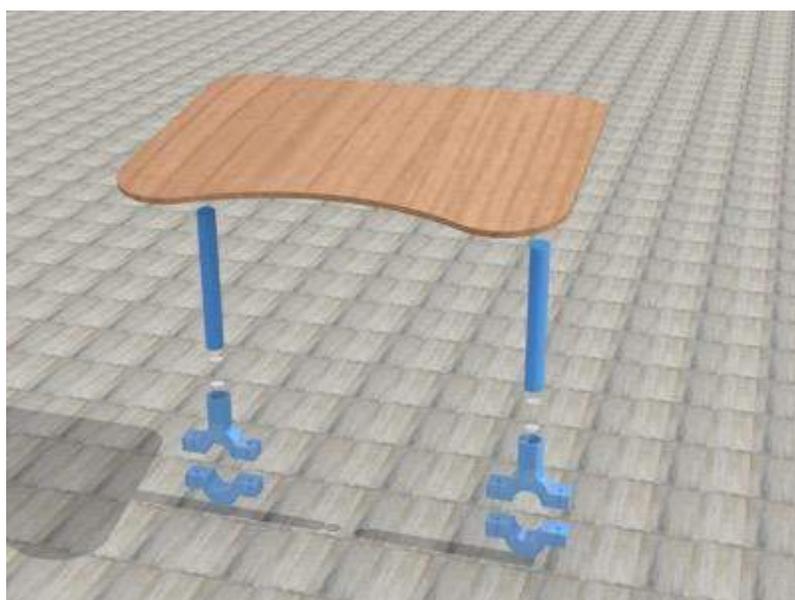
Vista explodida do modelo - Fonte: o autor.
